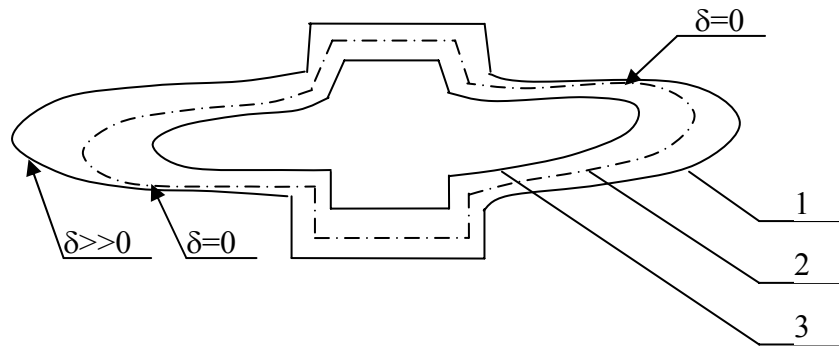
Неравномерное расположение заготовки относительно эталонной модели винта
